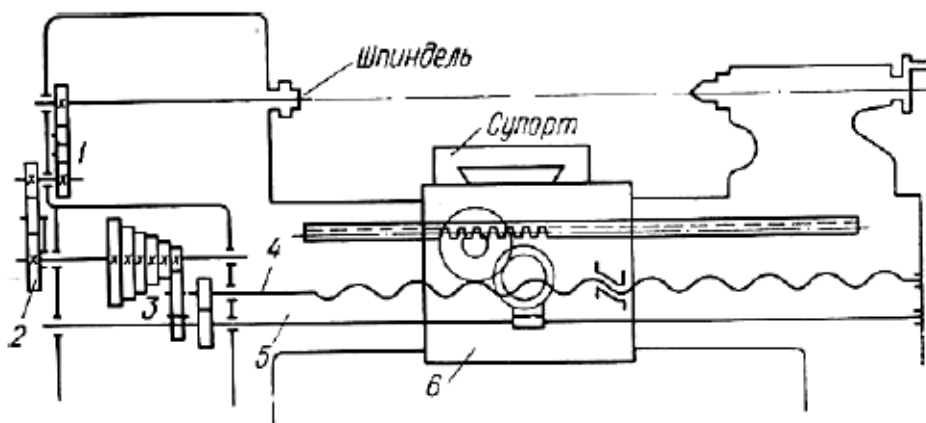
Схема механізму подачі 1, 2 – зубчасті колеса; 3 – коробка подач; 4 – ходовий гвинт; 5 – ходовий валик; 6 - фартух
